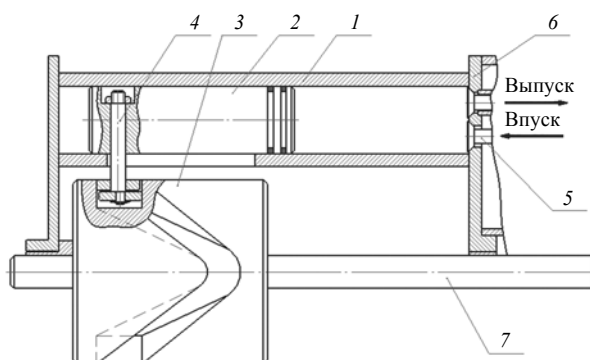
Схема, иллюстрирующая работу одного из цилиндров пневмопривода: 1 – рабочий цилиндр; 2 – поршень с уплотнительными кольцами; 3 – приводной барабан; 4 – ось с роликами; 5 – клапаны; 6 – корпус; 7 – приводной вал
